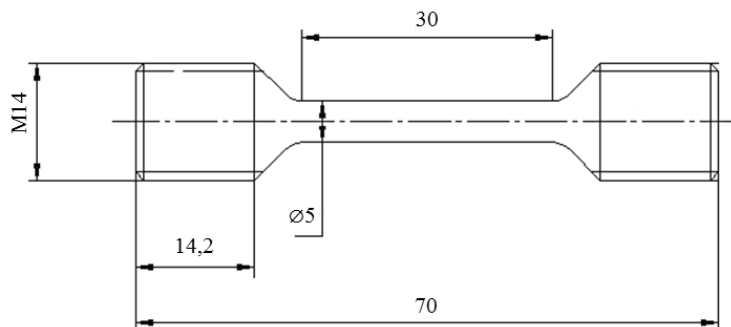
Типичная форма образца для испытаний жаропрочных сплавов
